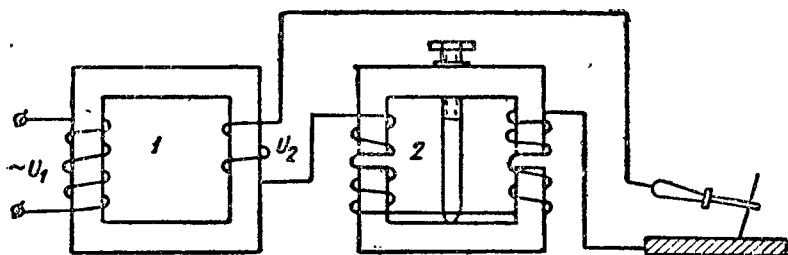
Схема сварочного трансформатора СТ-2:
